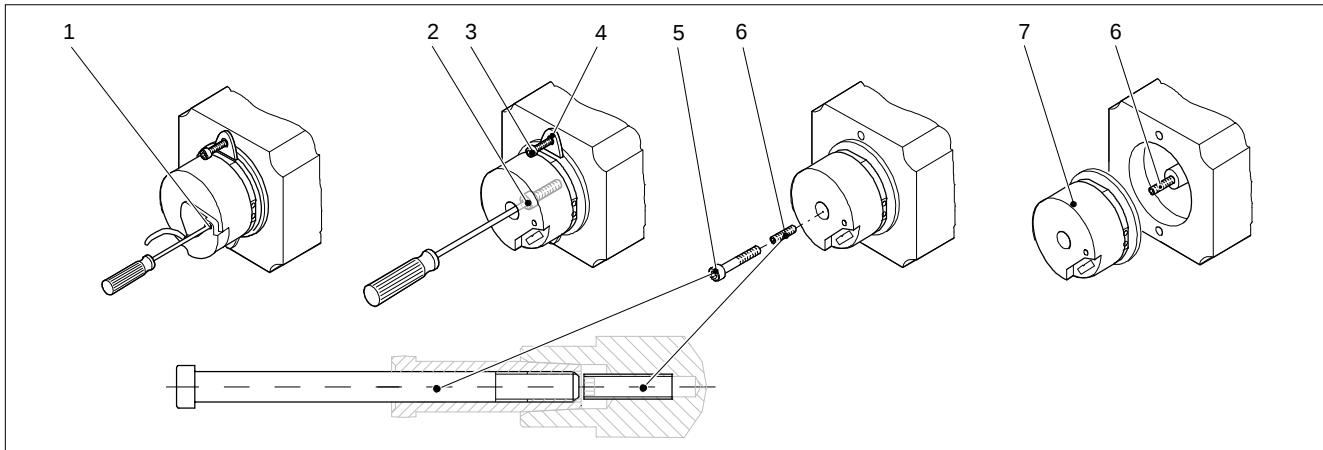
Abdrücken des Gebers mit Gewindestift und Schraube oder Sonderschraube
